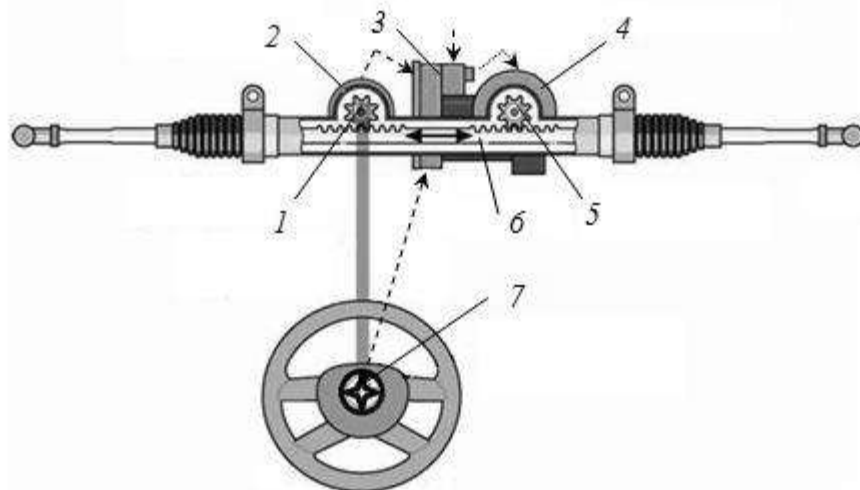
Схема рейкового електродвигуна з двома шестернями:
